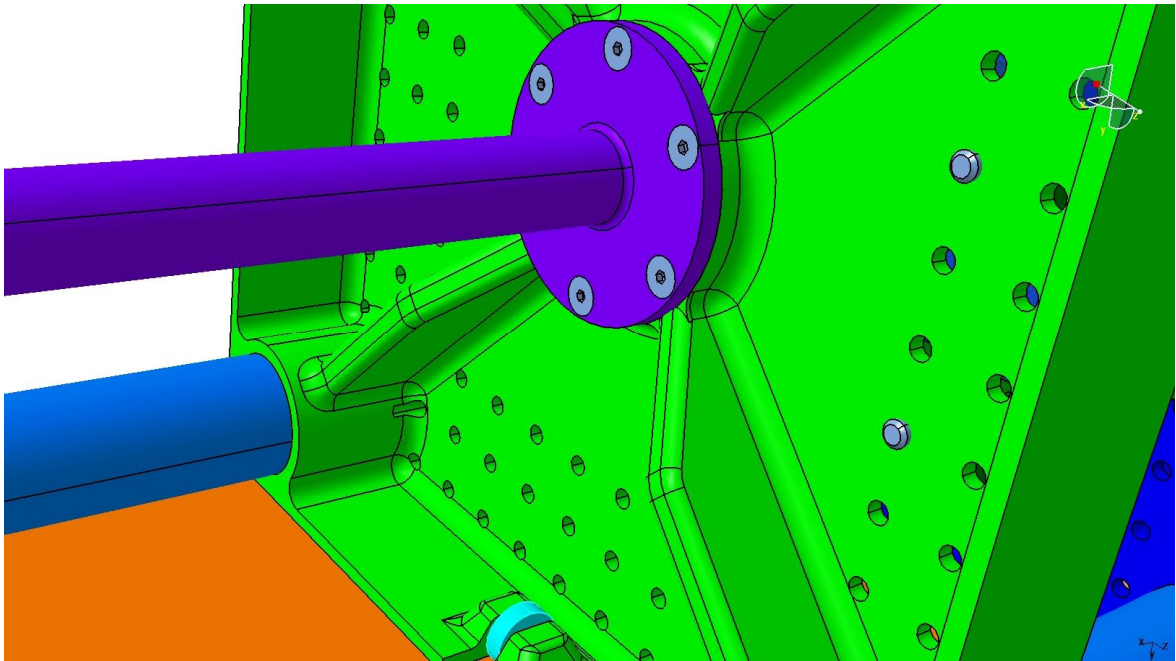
Pohled na zadní stranu laminátového ručního mechanismu
